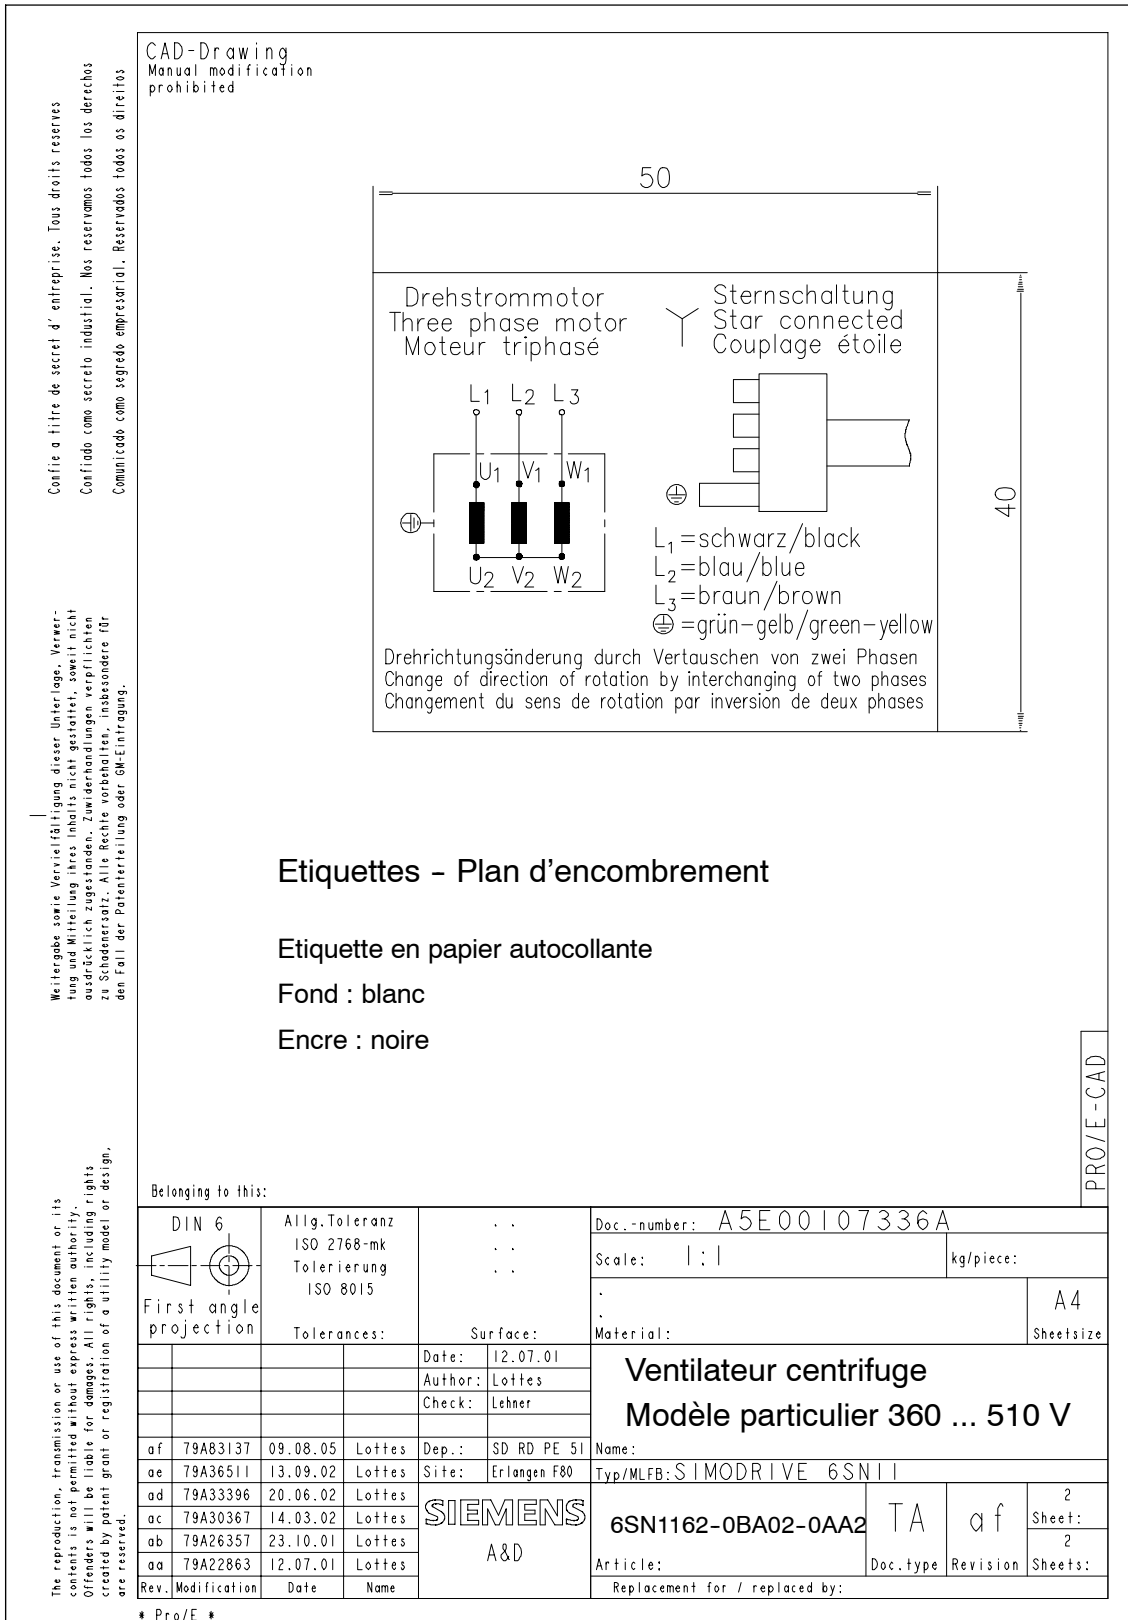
Ventilateur rapporté, 6SN1162-0BA02-0AA2; schéma de raccordement
